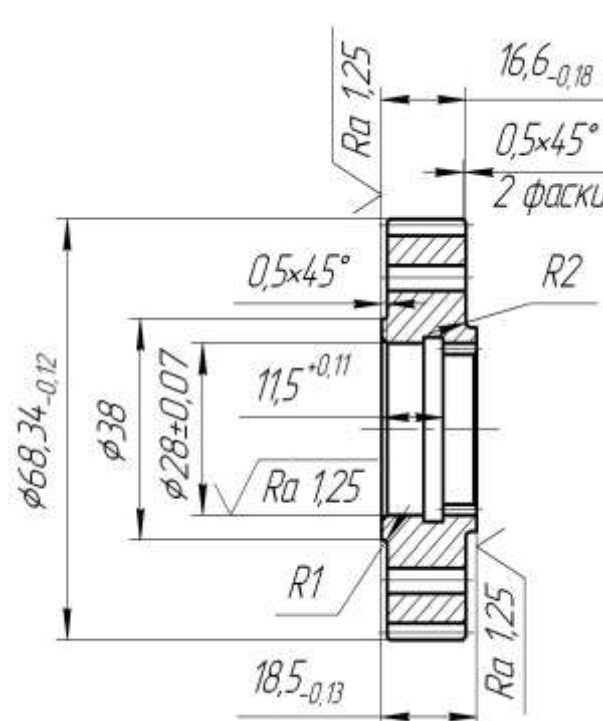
Шестерня ведомая 5-й передачи (заготовка)
